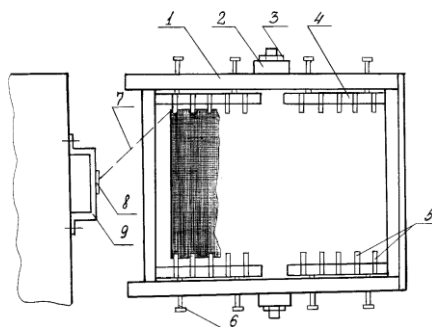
Вид сверху устройства для разматывания деталей трикотажных изделий
